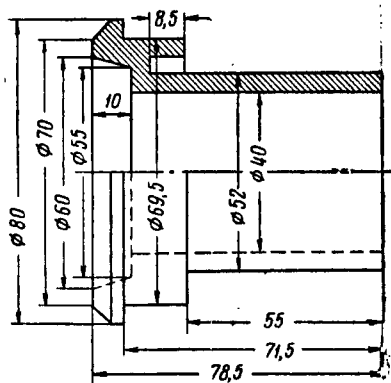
Заготовка переходной втулки для ДМГ-1500/50
